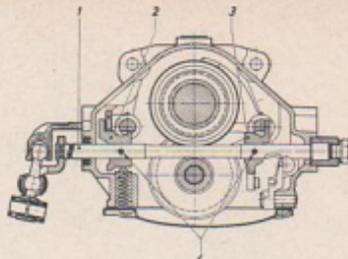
Änderung Schaltwelle in Getriebegehäuse
